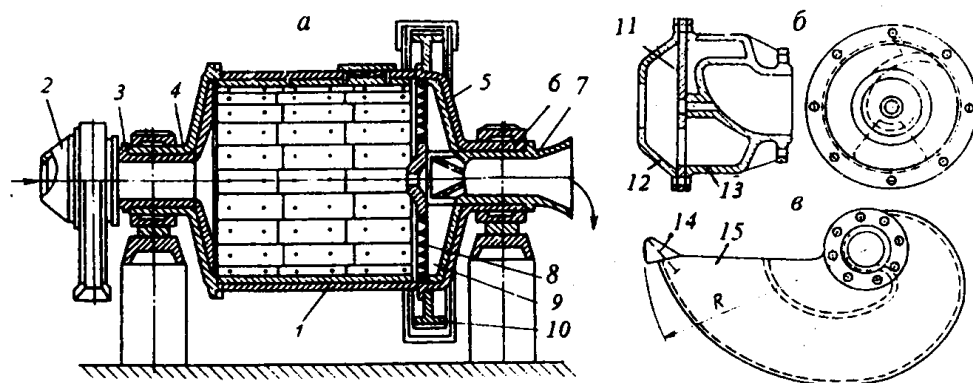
Схема шаровой мельницы с решеткой (а) и конструкции питателей: б и в — питатели соответственно барабанный и улитковый
